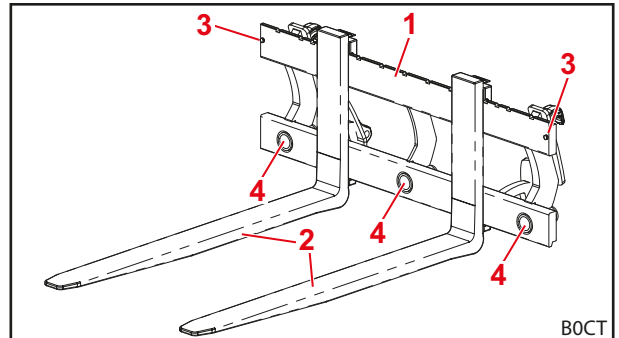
Конструкция вилок для поддонов HD с втулками для зубьев – вид спереди
